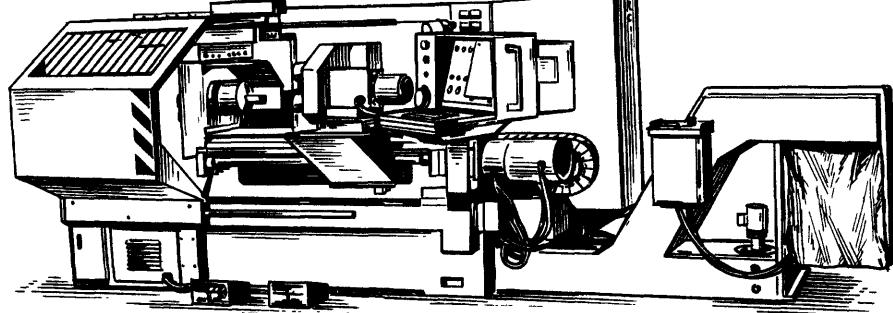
Токарный станок с ЧПУ модели 16А20Ф3
